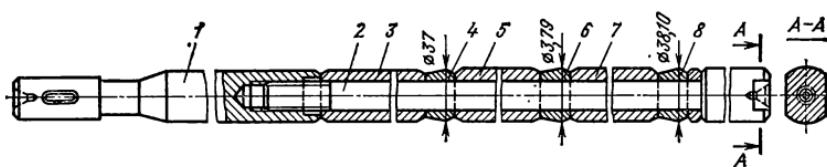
Деформирующая протяжка для обработки отверстия в цилиндре домкрата грузового автомобиля
